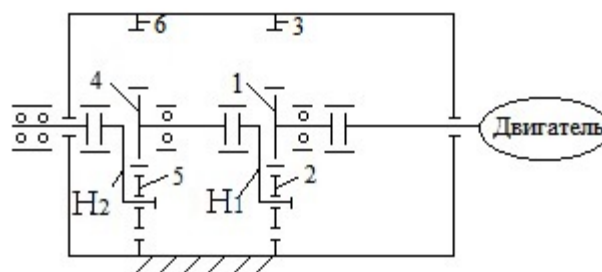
Кинематическая схема двухступенчатого планетарного редуктора: 1 – солнечное, центральное зубчатое колесо 1^{ой} ступени; 2 – сателлит; 3 – эпициклическое колесо 1^{ой} ступени; Н₁ – водило первой ступени; 4 – солнечное зубчатое колесо 2^{ой} ступени; 5 – сателлит; 6 – эпициклическое колесо 2^{ой} ступени; Н₂ – водило второй ступени
